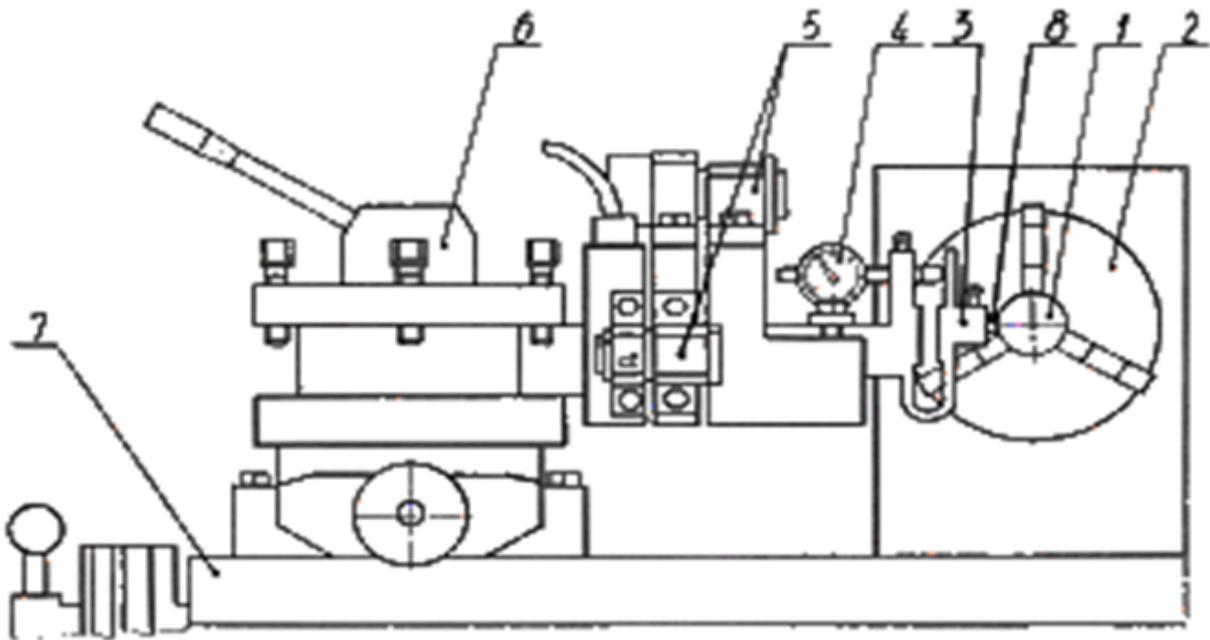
Схема экспериментальной установки: 1 — образец; 2 — шпиндель станка; 3 — динамометр; 4 — стрелочный индикатор; 5 — державка; 6 — резцедержатель станка; 7 — салазки; 8 — контртело
